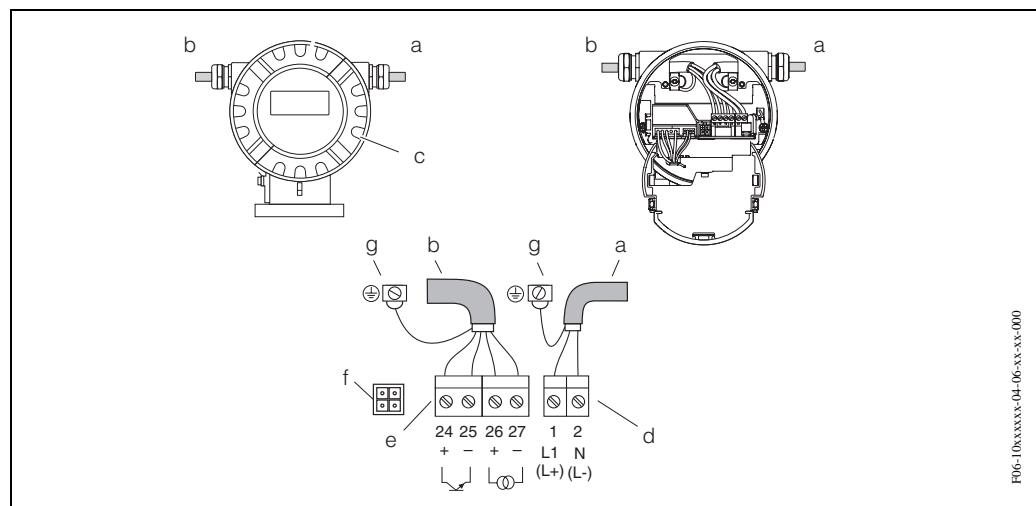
Подключение преобразователя (алюминиевый корпус). Поперечное сечение кабеля: макс. 2.5 мм²
